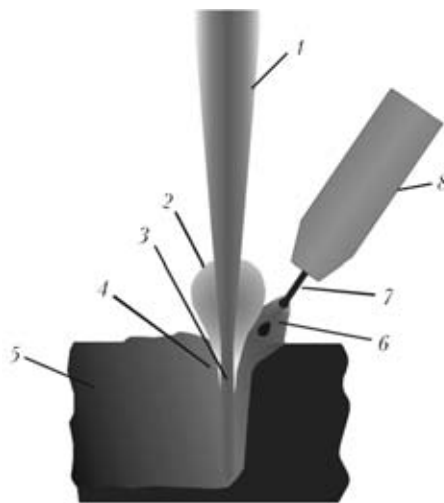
Схема гибридной лазерно-дуговой сварки: 1 — лазерный луч; 2 — плазма; 3 — парогазовый канал; 4 — жидкая ванна; 5 — свариваемый материал; 6 — сопло GMA; 7 — присадочная проволока; 8 — горелка GMA
